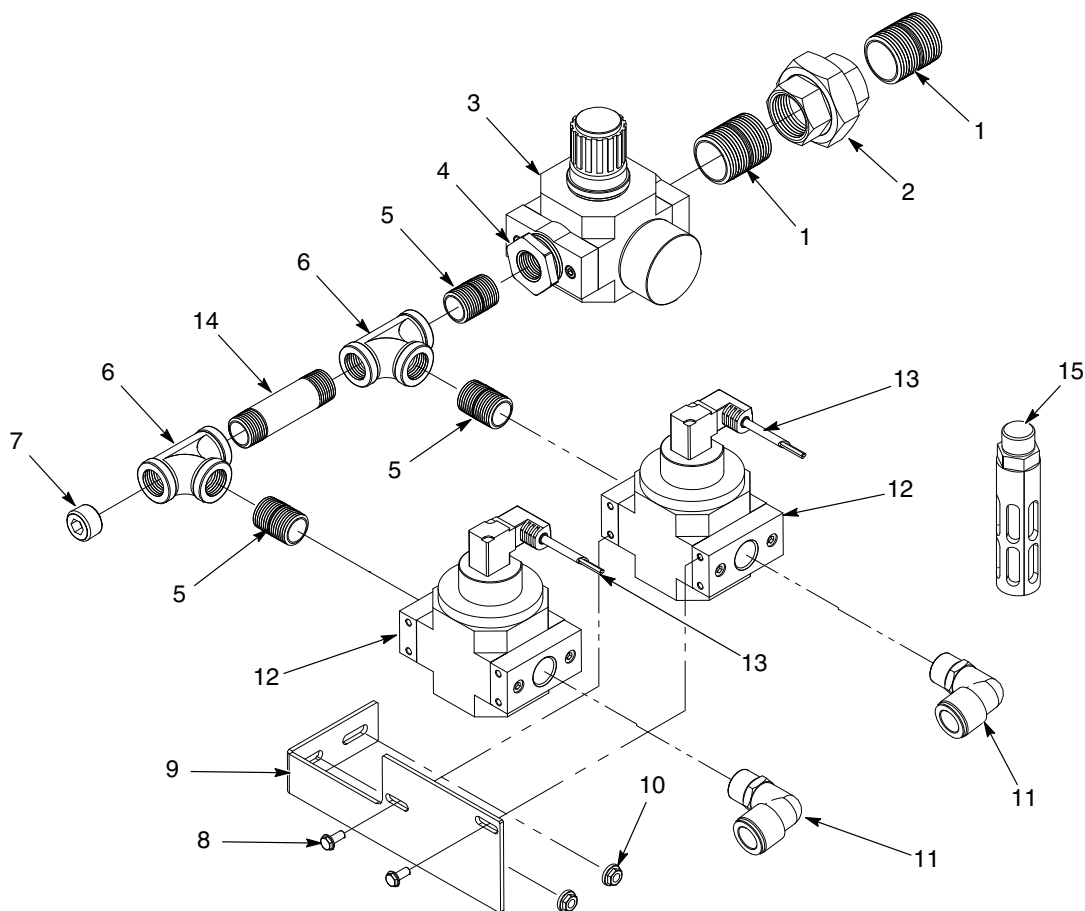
Spülventilbaugruppe - Konfiguration mit zwei Lanzen
